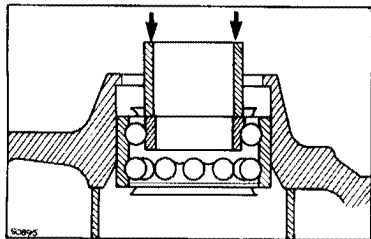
Выбивание подшипника ступицы из поворотного кулака
